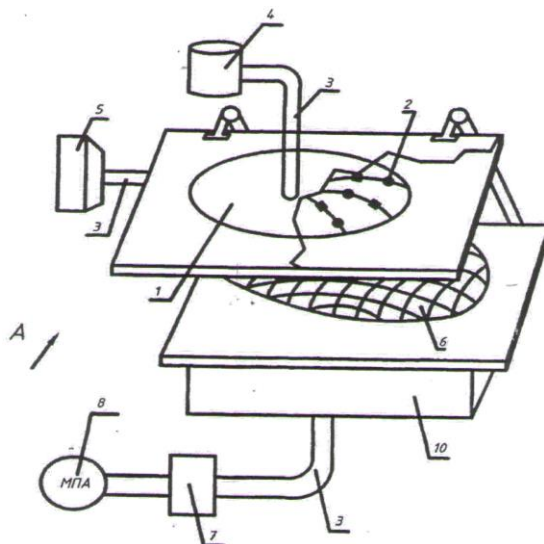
Общий вид установки для формования объемных деталей одежды
